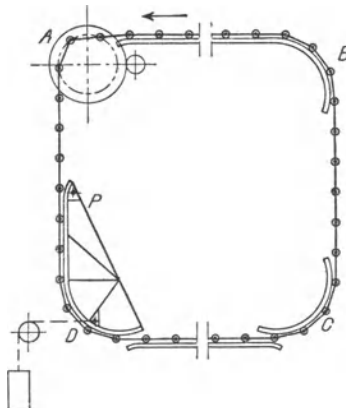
Spannvorrichtung bei einem Förderer mit Viereckslauf. Alte Bauart.
